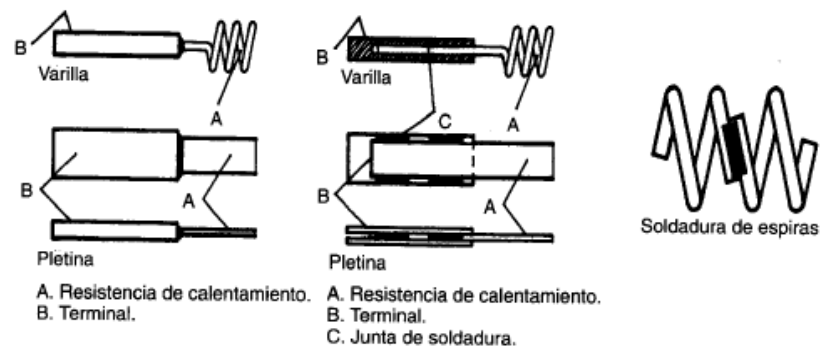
13: Soldadura de terminales y resistencias. (Astigarraga Urquiza, 1994)
